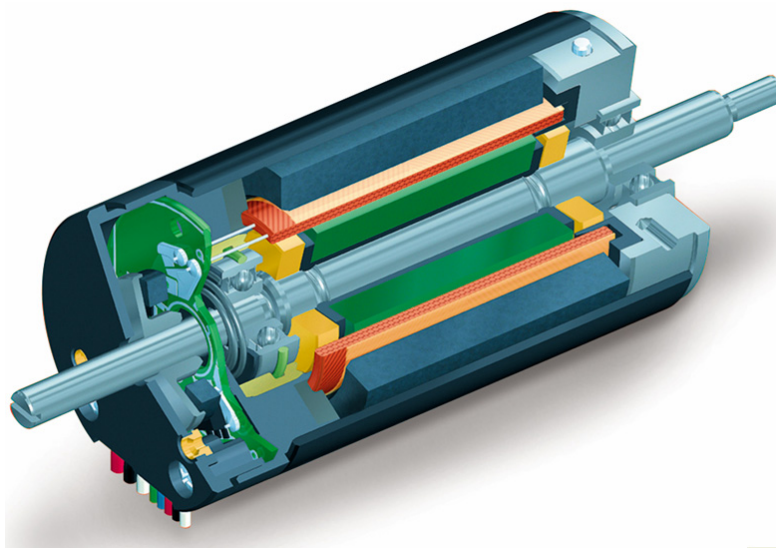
Příklad vícepólového rotoru u DC motoru – mechanický komutátor v levé části
